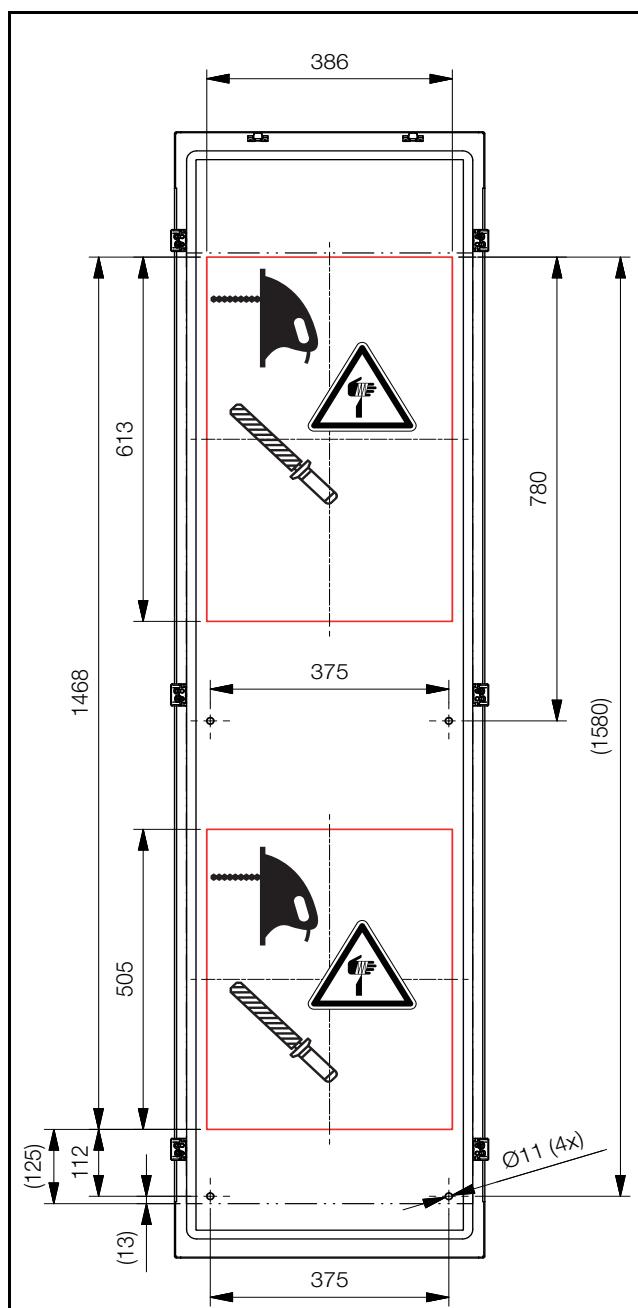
Escotadura de montaje para armarios de 500 mm de profundidad
